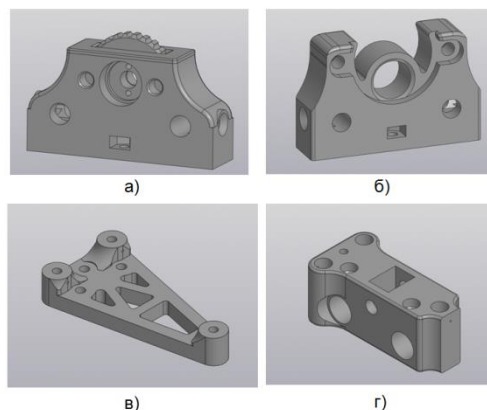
Элементы столика: опоры для направляющих с ручным управлением перемещения (а); с возможностью закрепления мотора (б); предметная платформа с крепежами для держателей для предметного стекла (в); каретка одной из осей (г)
